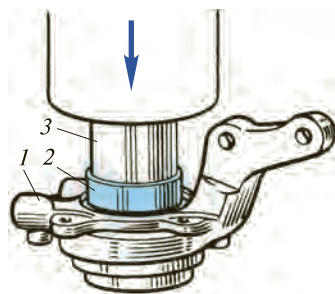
Запрессовка подшипника в поворотный кулак:
